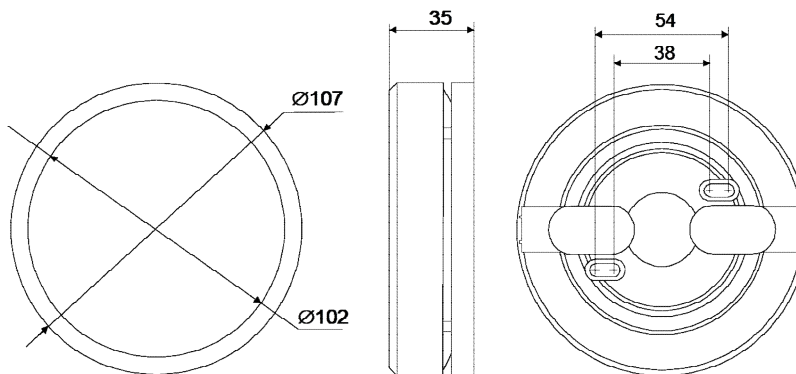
Габаритные размеры и расположение крепежных отверстий оповещателя DBS 1224B4W
